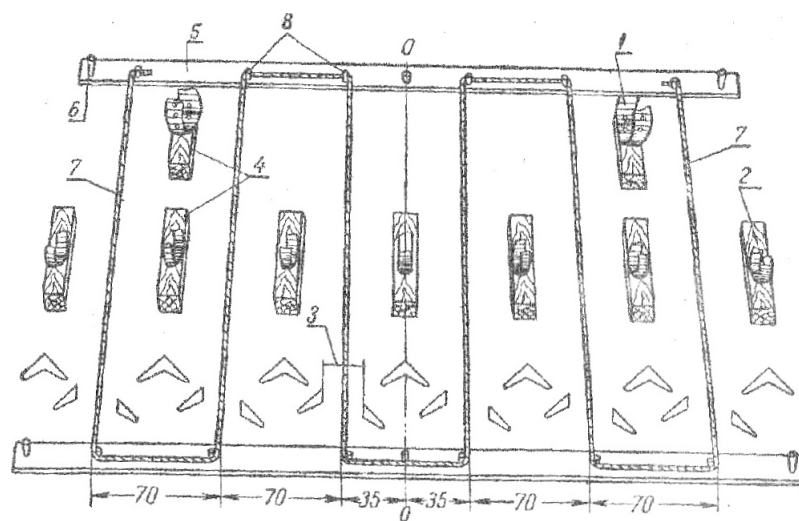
Схема установки робочих органів культиваторів: 0-0 - осьова лінія культиватора; 1 - опорне колесо рами; 2 - копіюючі колеса; 3 - захисна зона; 4 - дерев'яні бруски; 5 розмічальні дошки; 6 - кілочки; 7 - шнур; 8 - цвяхи.
